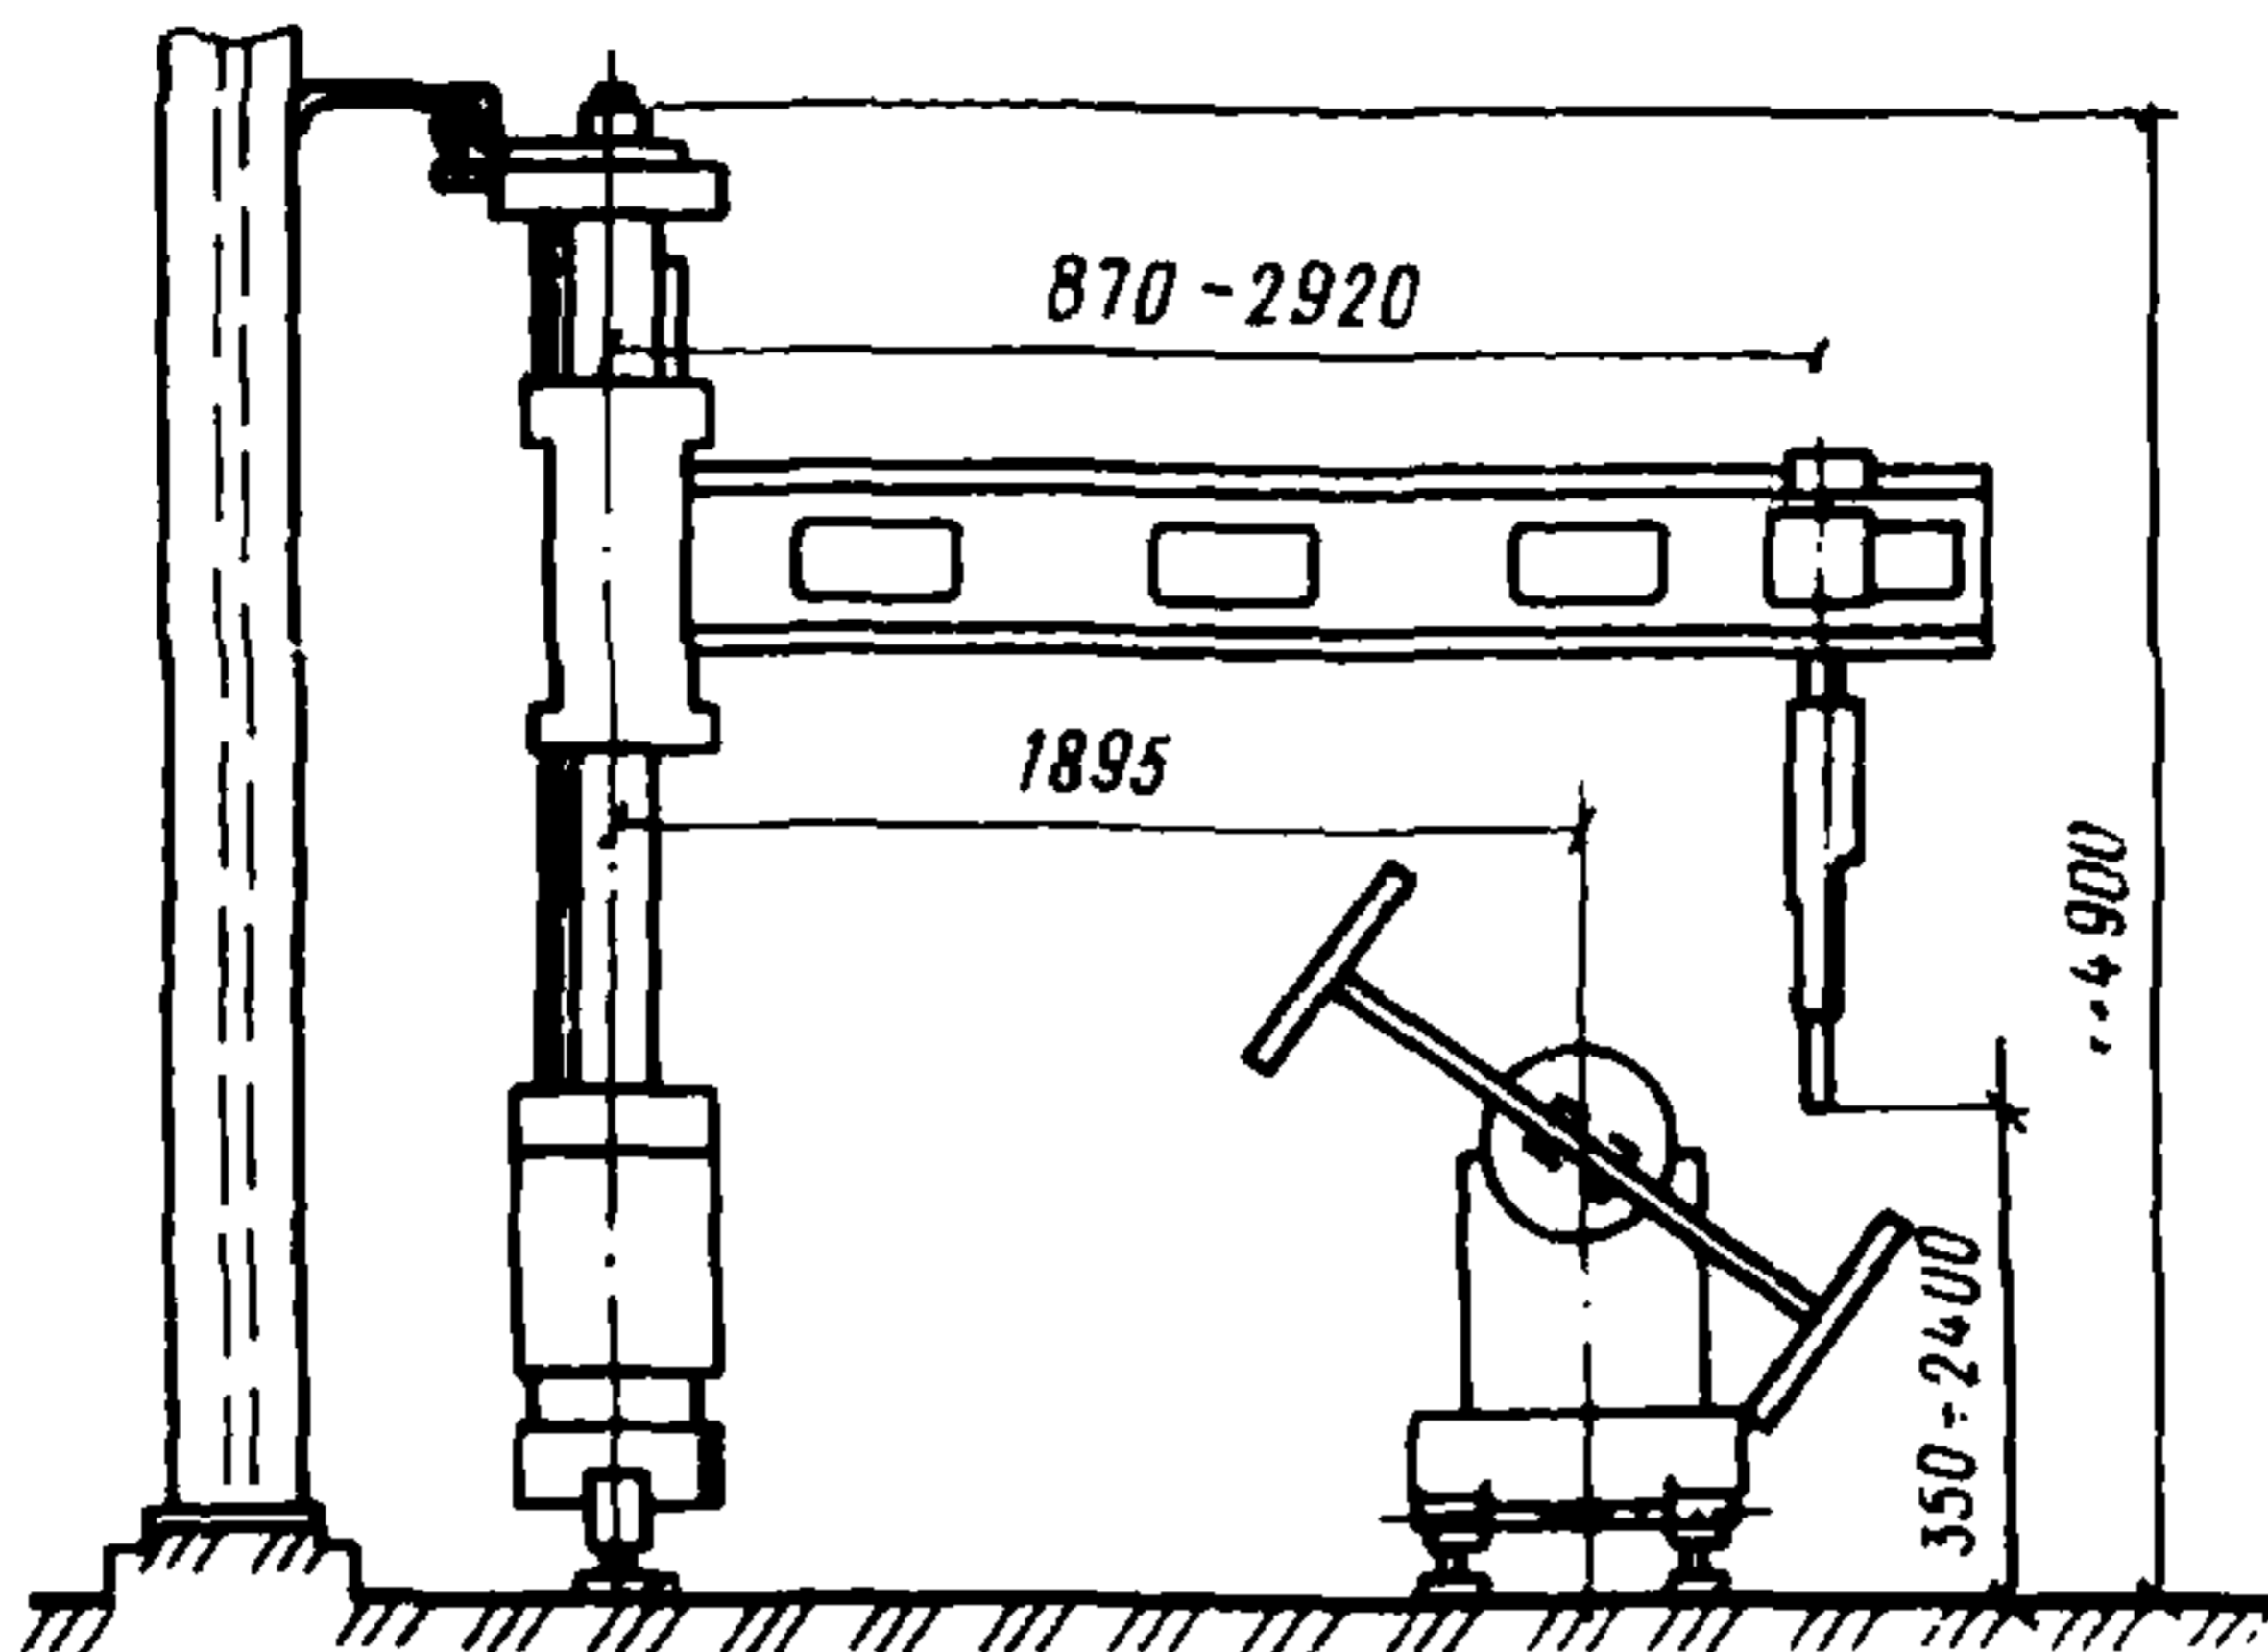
Велотележка с кантователем для сварки стержней двутаврового сечения
